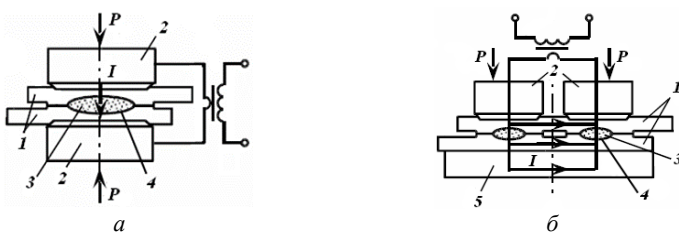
Принципиальные схемы точечной сварки:
